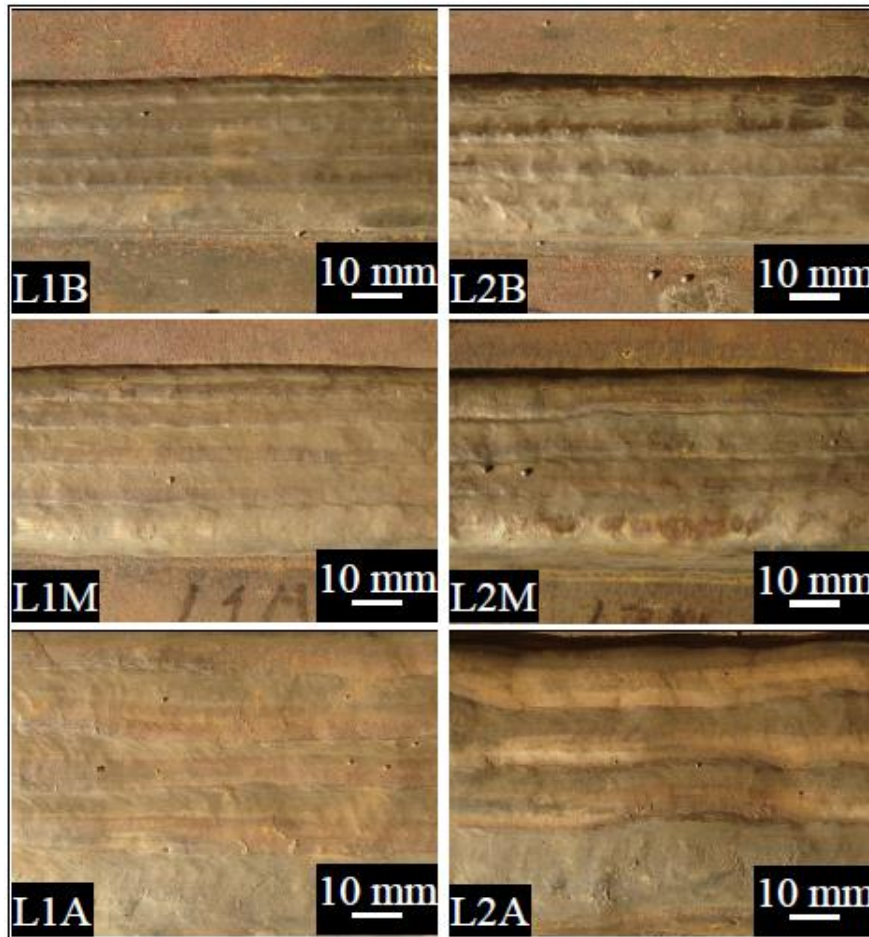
Vista superior de cordones de soldadura LDSS.
